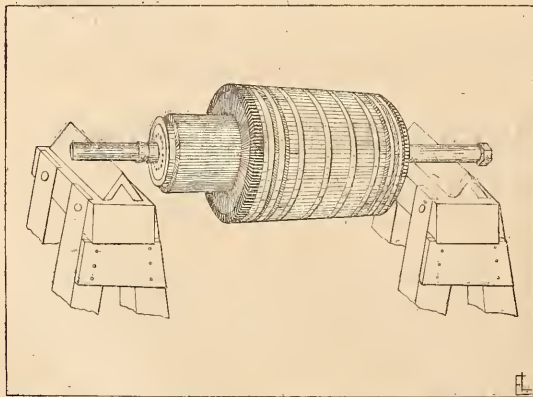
Équilibrage d'un induit par installation de fortune.
